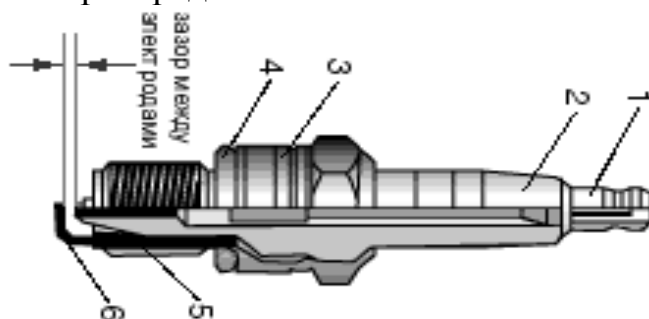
Свеча зажигания 1 - контактная гайка; 2 - изолятор; 3 - корпус; 4 - уплотнительное кольцо; 5 - центральный электрод; 6 - боковой электрод
